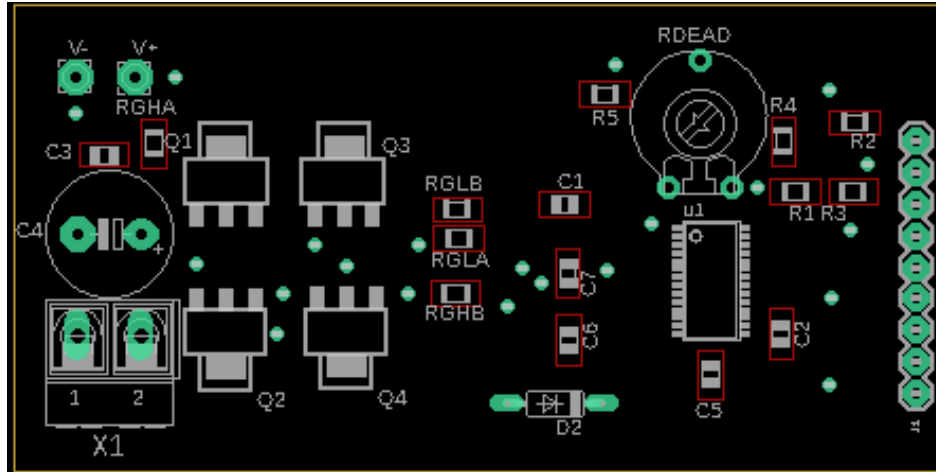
Posicionamento dos componentes que constituem o inversor no PCB.
